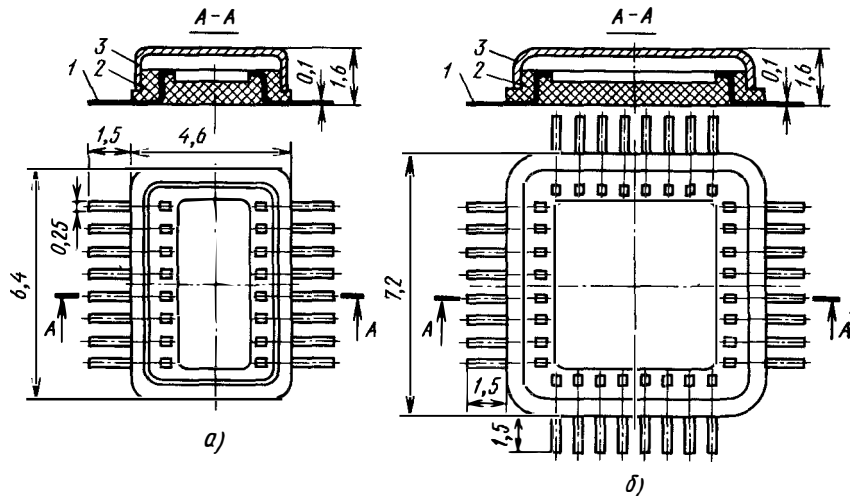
Металлополимерные корпуса ИС с планарными выводами (на виде сверху крышки условно не показаны): а—16-выводный; б—32-выводный; 1—никелевые выводы; 2—полимер; 3—металлическая крышка
